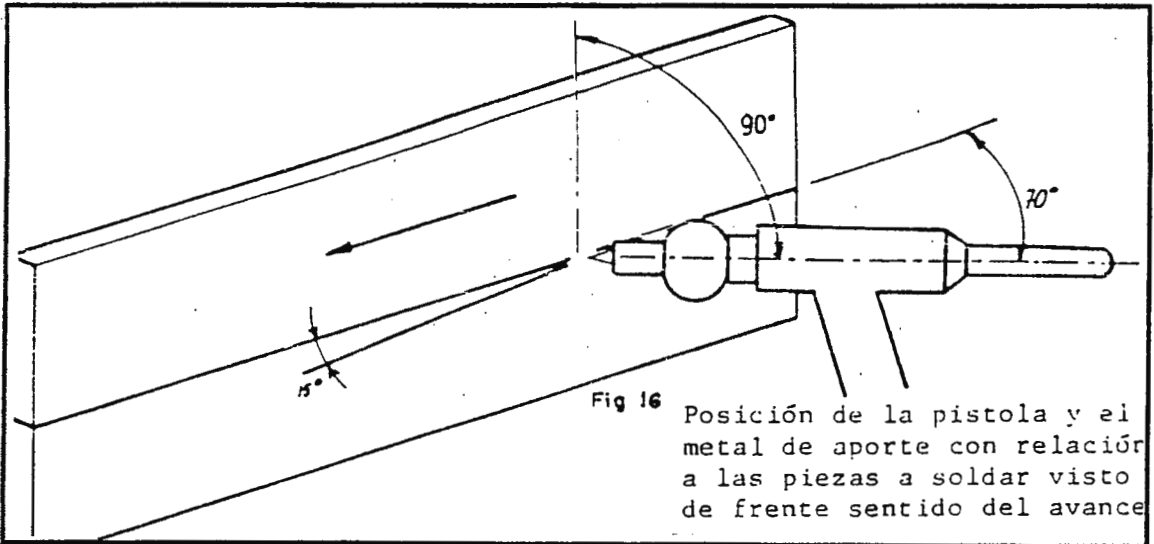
Posición de la pistola y el metal de aporte con relación a las piezas a soldar y visto de frente sentido del avance
